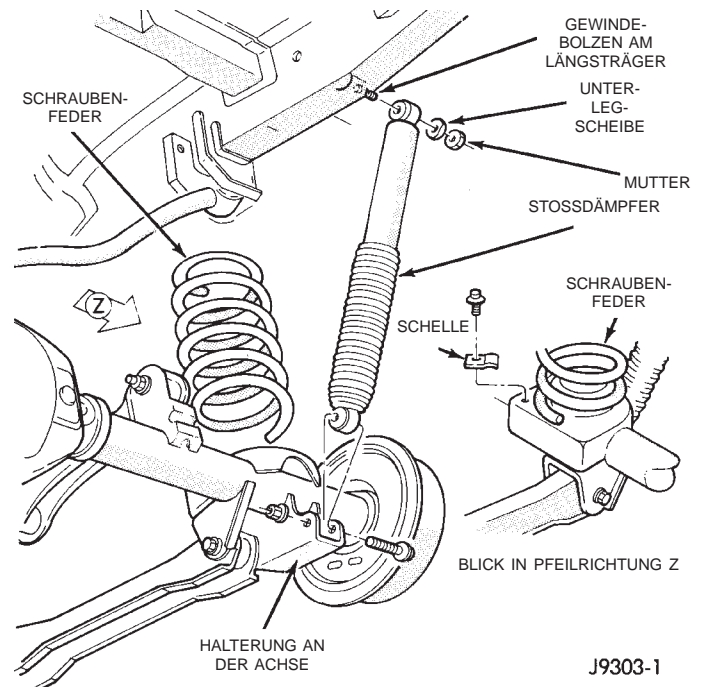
Schraubenfeder und Stoßdämpfer hinten
